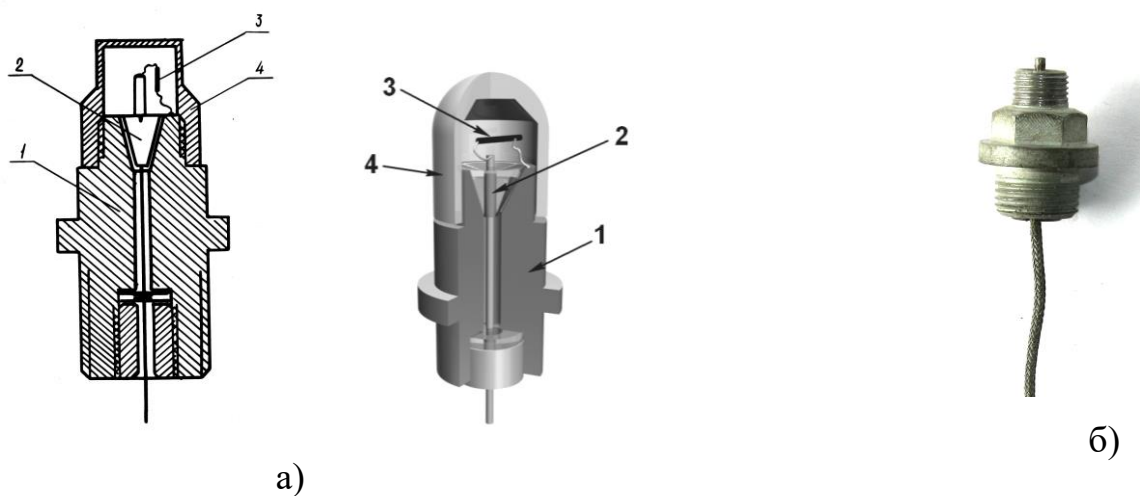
Конструкція (а) і зовнішній вигляд (б) датчика гідростатичного тиску: 1 – корпус; 2 – герметичний струмовідвід; 3 – чутливий елемент на основі НК GaSb; 4 – захисний ковпачок [386]
